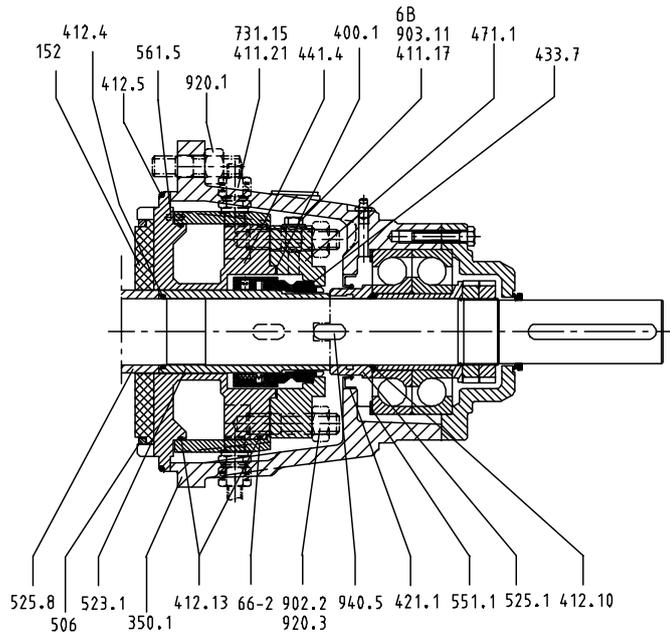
Desmontaje del cierre mecánico enfriado por agua
